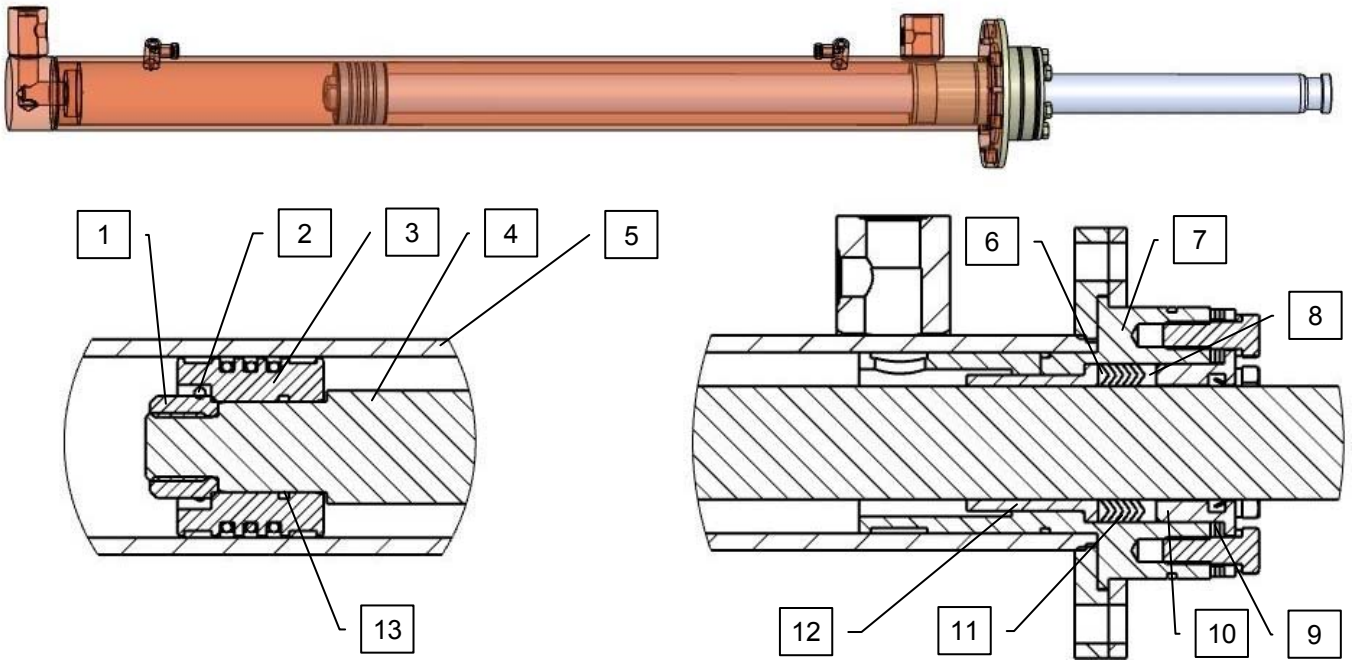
Гидроцилиндр: 1 – гайка; 2 – фиксатор; 3 – поршень; 4 – шток; 5 – цилиндр; 6 – кольцо опорное; 7 – крышка; 8 – кольцо прижимное; 9 – прокладка; 10 – фланец; 11 – манжета; 12 – втулка; 13 – кольцо.
